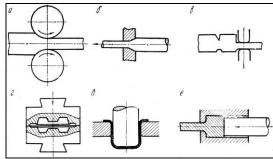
Схемы обработки заготовок давлением: а) прокатка; б) волочение; в) ковка; г) объёмная штамповка; д) листовая штамповка; е) прессование
